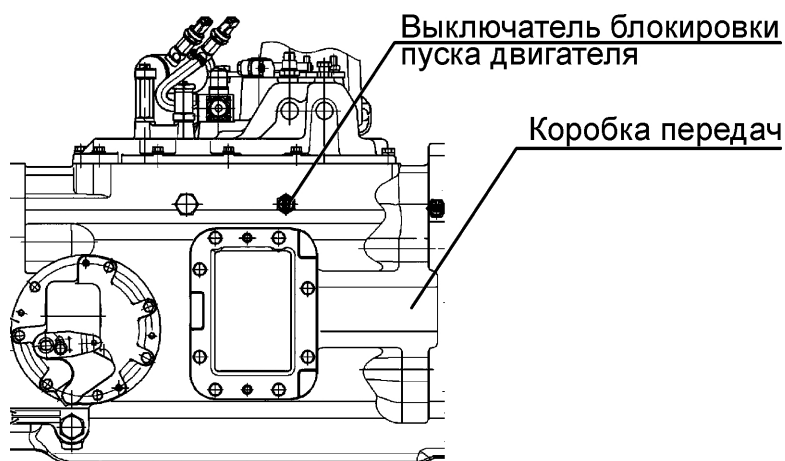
Выключатель блокировки пуска двигателя
